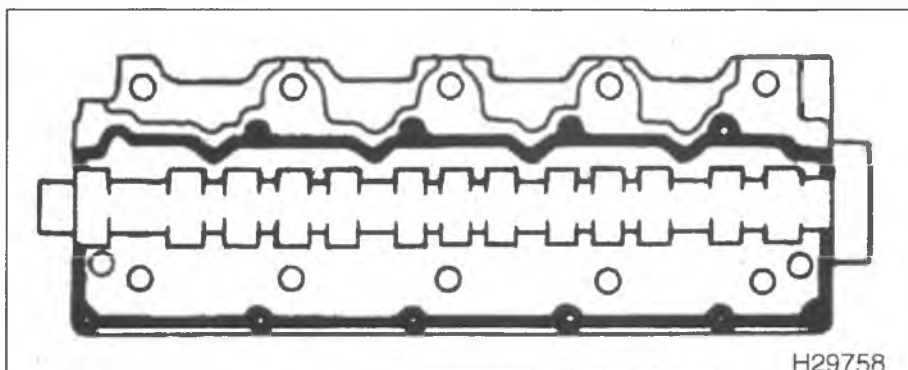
Нанесите валик герметика на выделенную зону стыковочной поверхности корпуса подшипников распределительного вала
